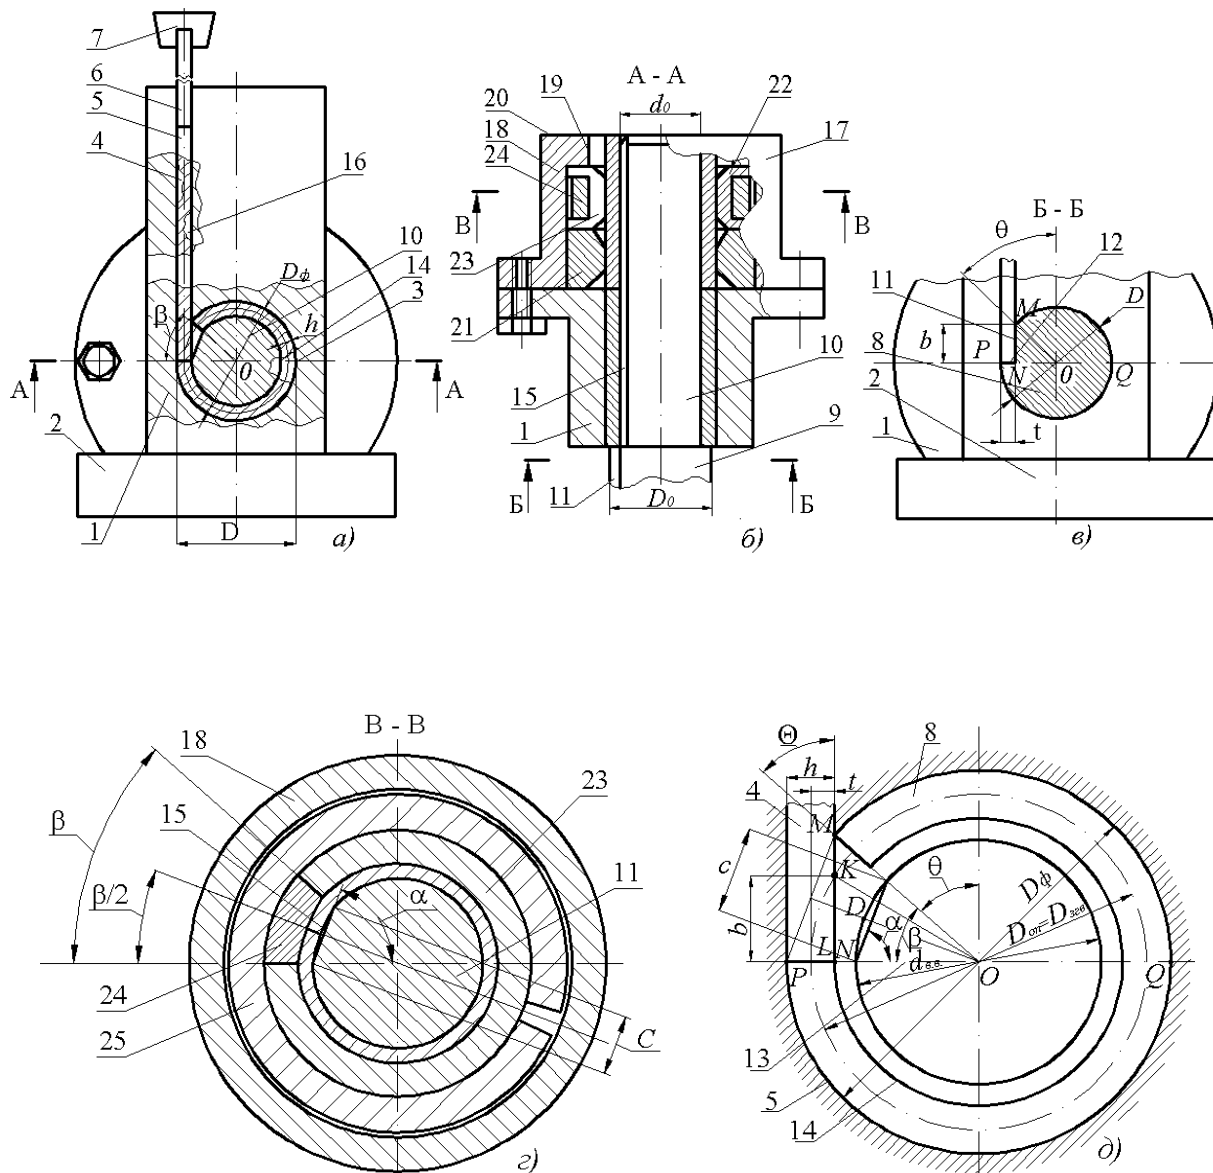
Пристрій для формування і калібрування згортих втулок:
